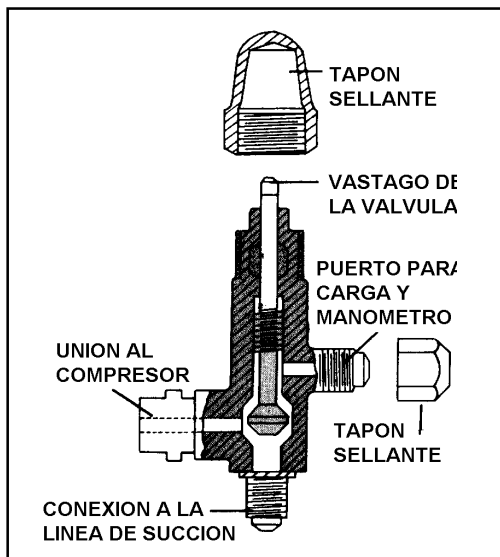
Válvula de servicio para compresor hermético, soldable.
